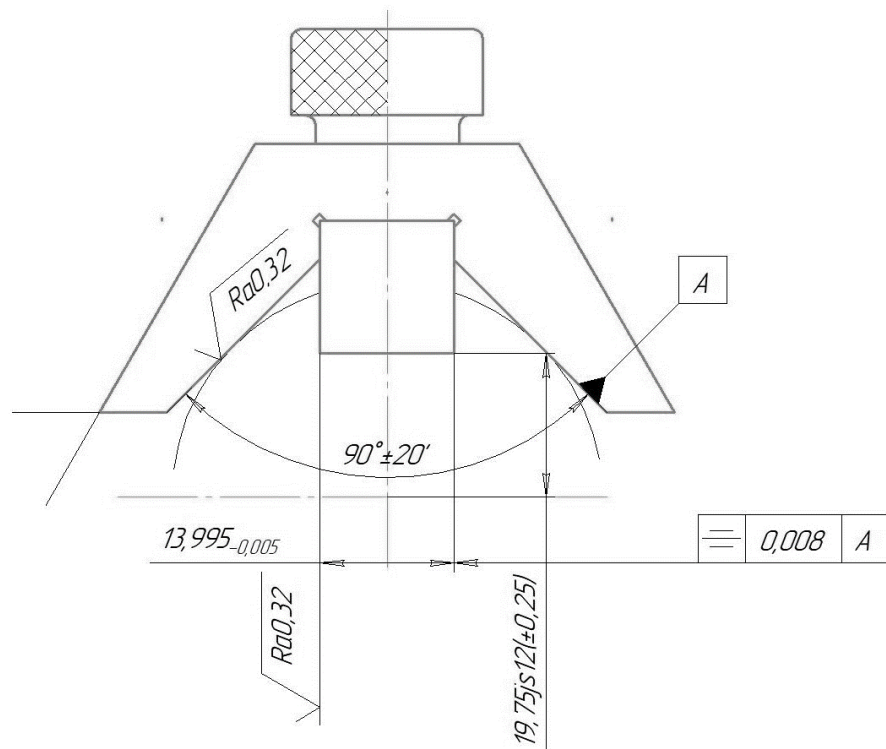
Размеры шпоночного калибра-призмы
